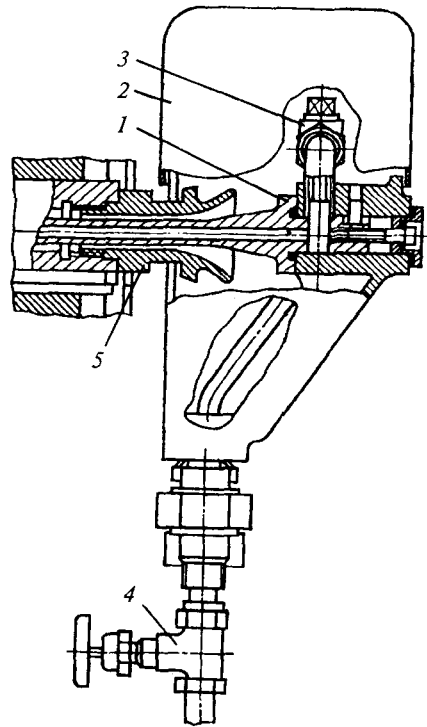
Устройство охлаждения вальца станка 3М2
